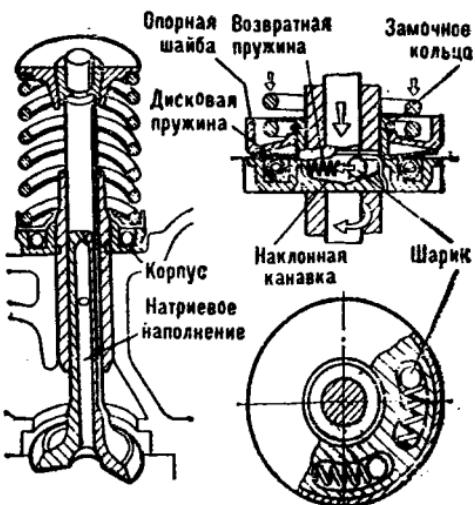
Устройство для поворота выпускного клапана двигателя ЗИЛ-130
